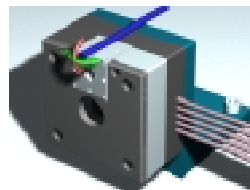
PENTOR T-452-00, Z-700-00; Kabelführung links
